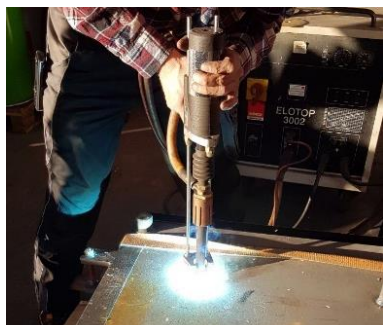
Anschweißen der Kopfbolzendübel mittels Bolzenschussgerät.
